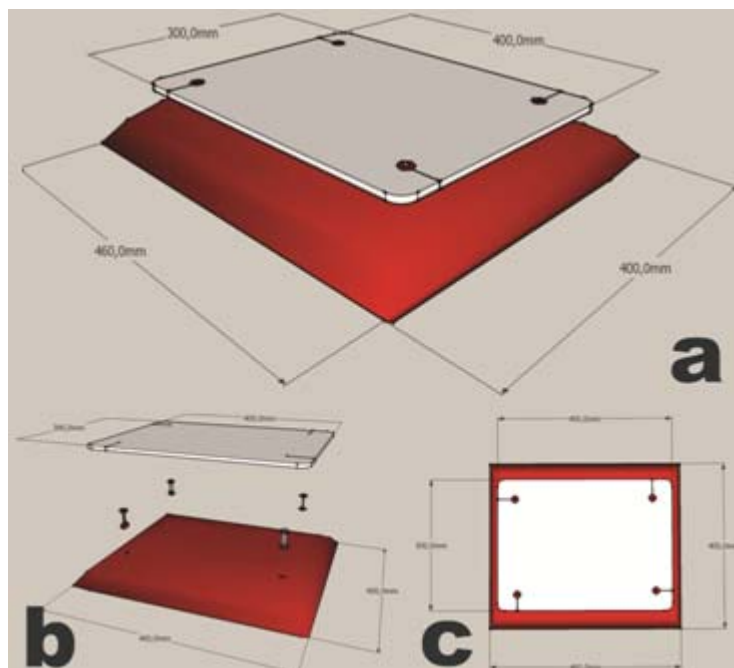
Protótipo: a) dimensões da peça, b) desenho explodido e c) vista superior.
